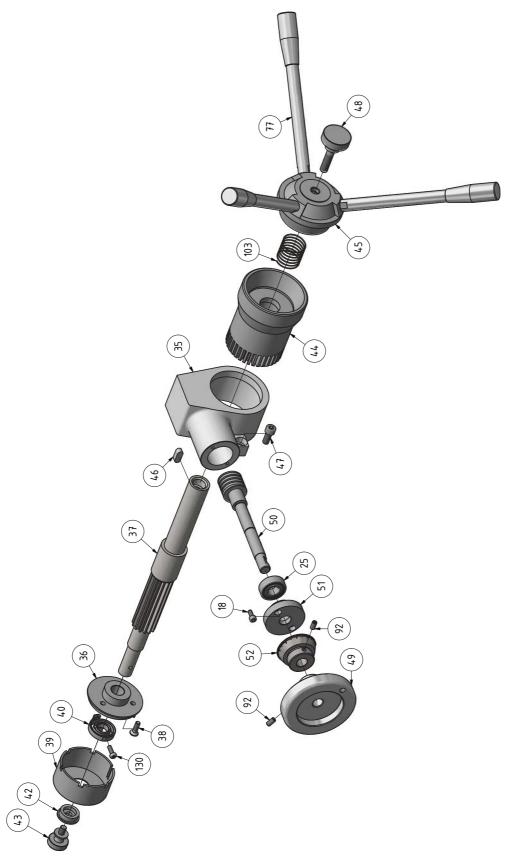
Fräskopf 5 von 6 - Milling head 5 von 6
